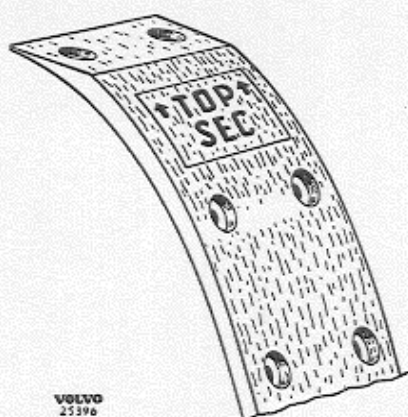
Hinterer Bremsbelag für die Vorderräder.
